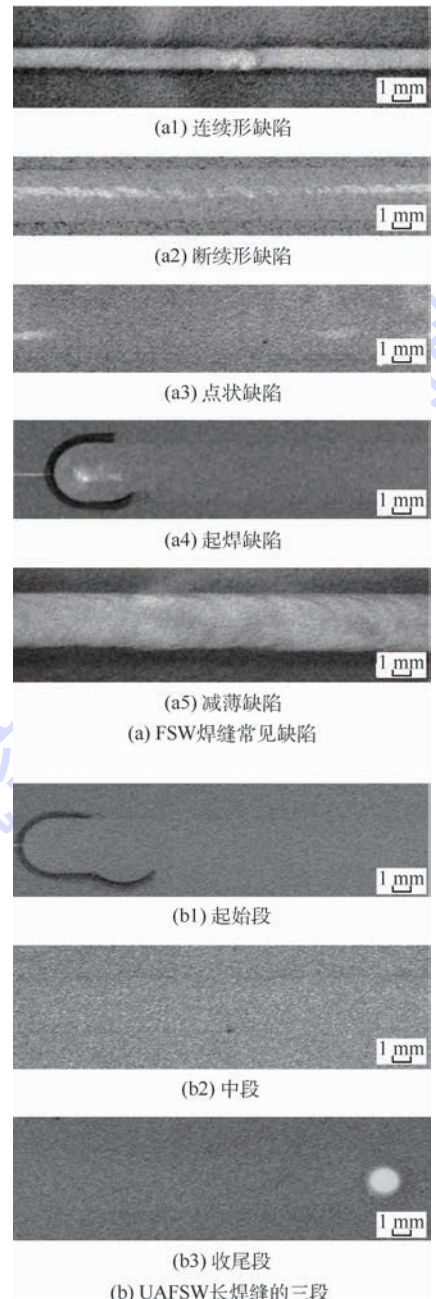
FSW 与 UAFSW 焊缝的 X 射线无损检测照片
